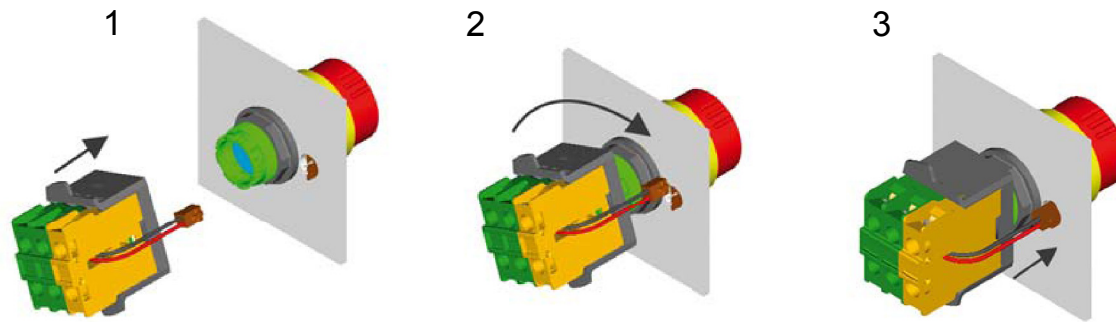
Montage KE...B (Abbildung zeigt Variante mit Beleuchtungsanschluss)
